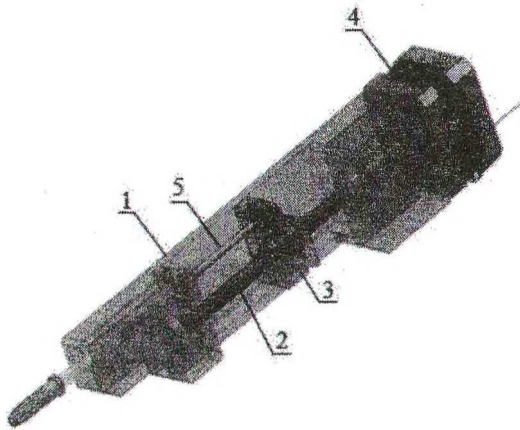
Устройство дозирования капли: 1 – корпус; 2 – вращающийся вал с резьбой; 3 – каретка; 4 – шаговый электродвигатель; 5 – поршень
